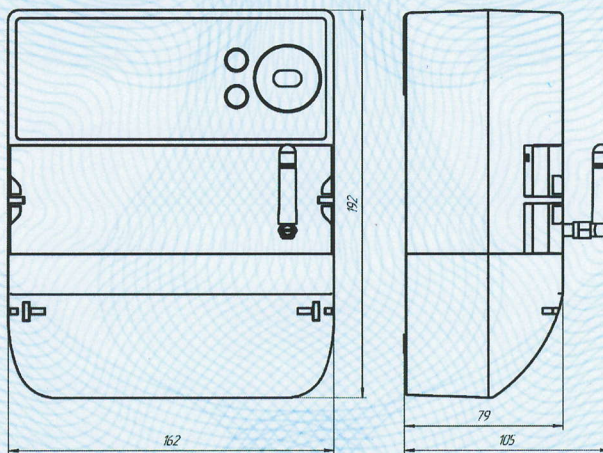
Габаритні розміри лічильника у корпусі 10м, мм
